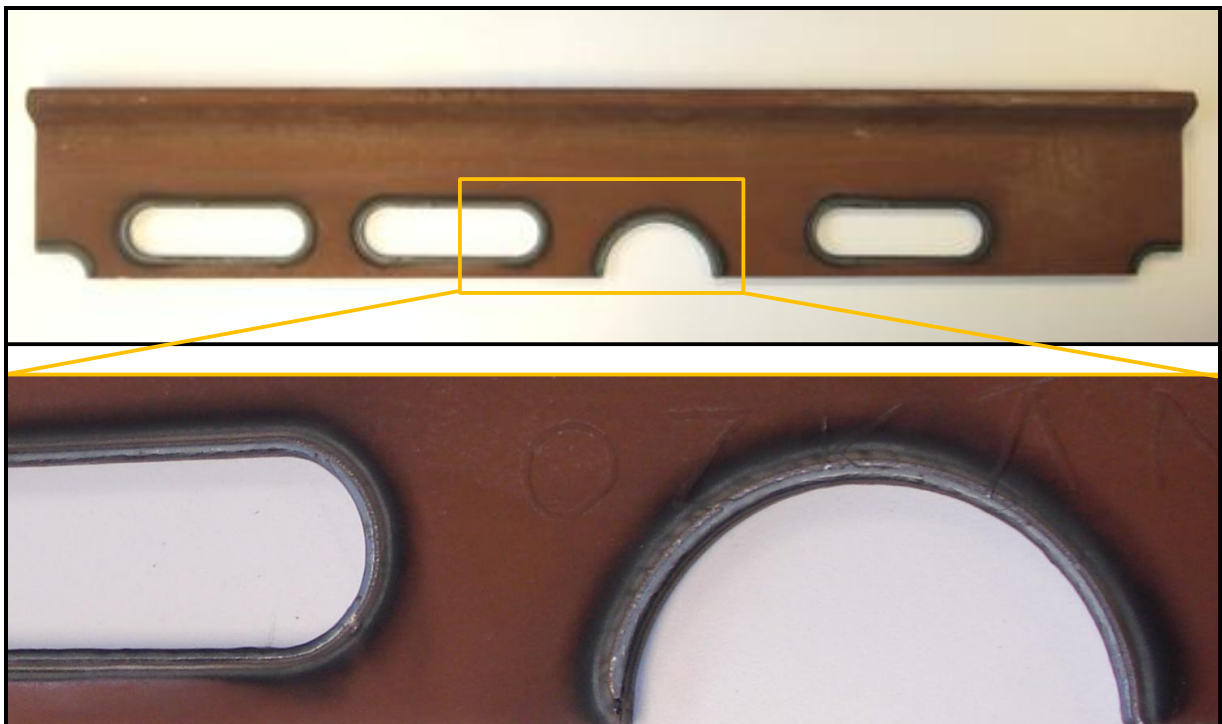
Demonstratorbauteil für das thermische Kanterunden mit dem Plasmaschweißverfahren in der Profilschneidanlage
